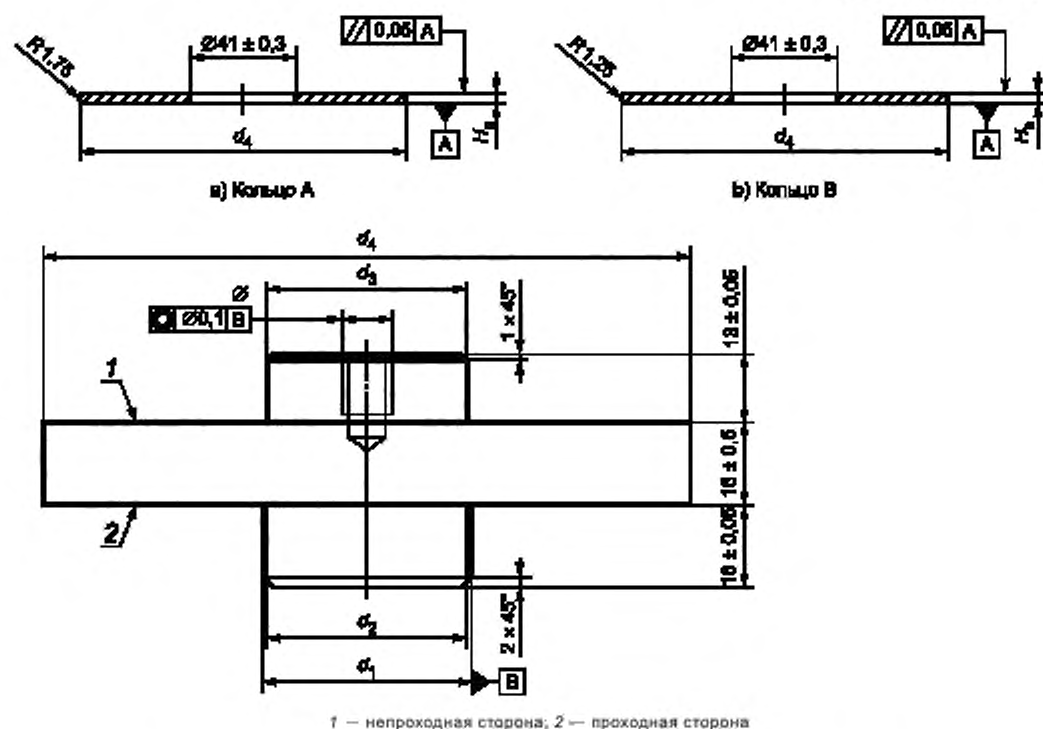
Размеры калибра для проверки соединителя с внутренней резьбой
